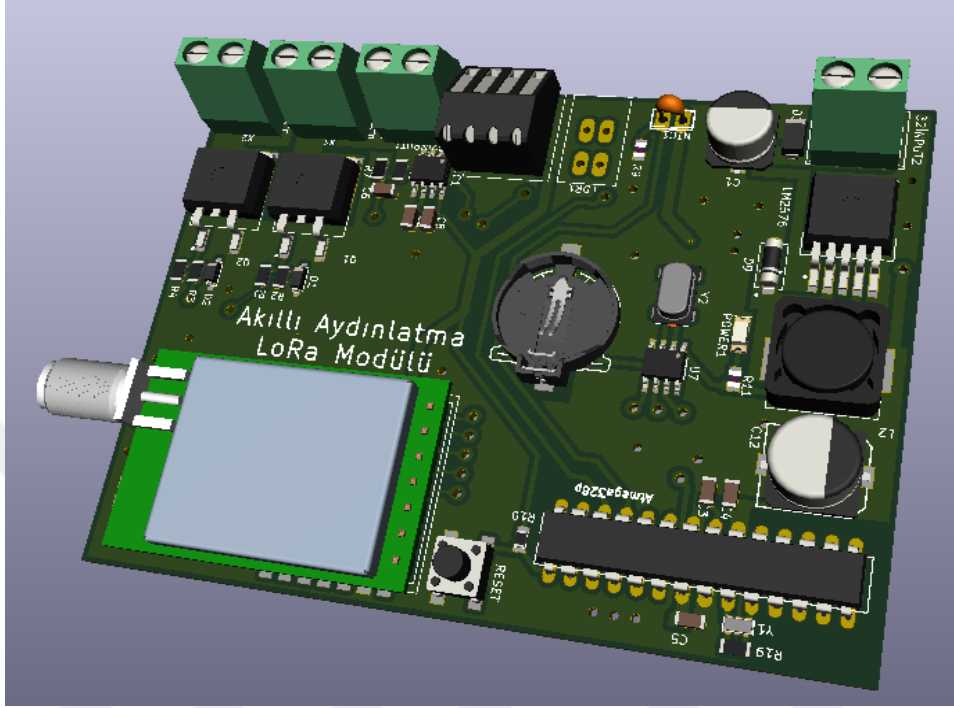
Akıllı aydınlatma sensörler ve LoRa PCB modülü footprint
